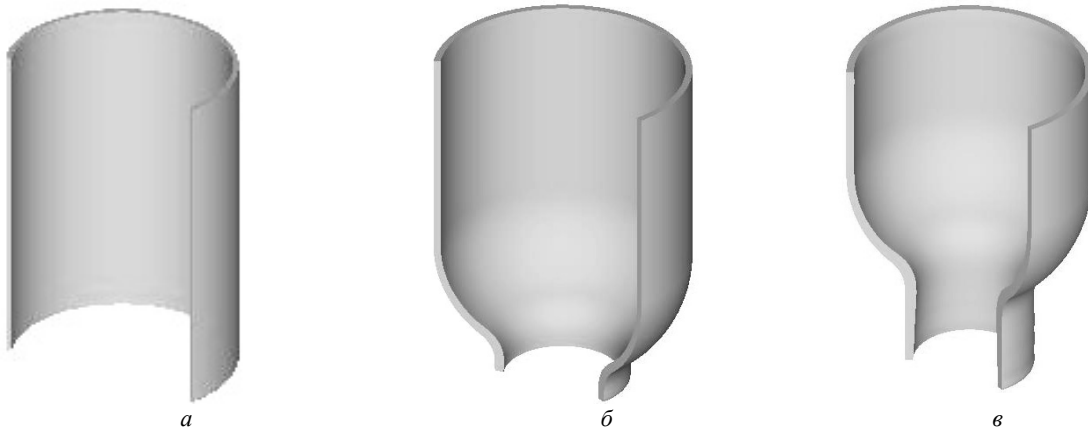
Вихідна заготовка в розрізі (а) та zdeформовані заготовки з протитиском $q=0$ (б), $q=70$ МПа (в)
